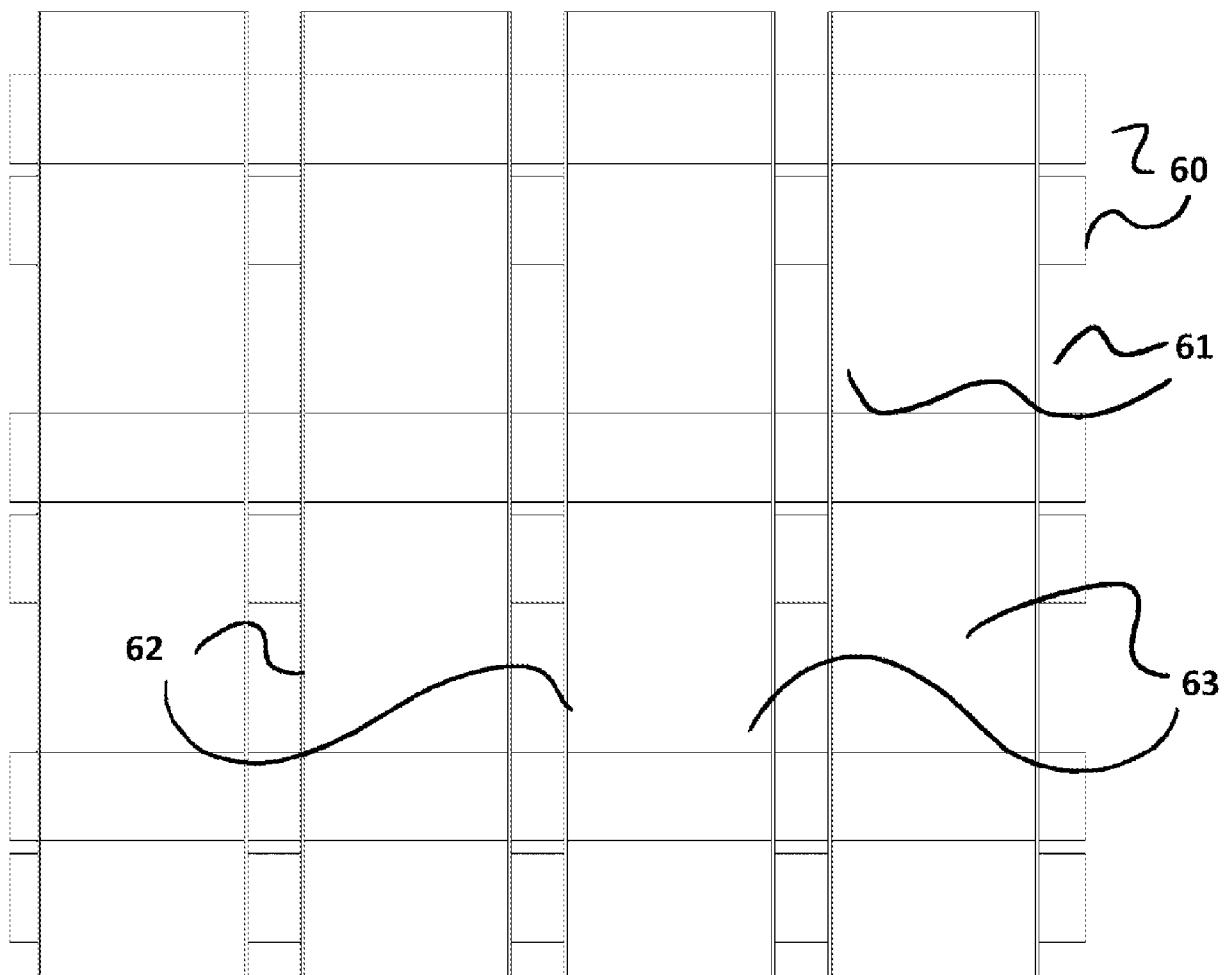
vista frontal detallada del radiador de aletas y tubos
